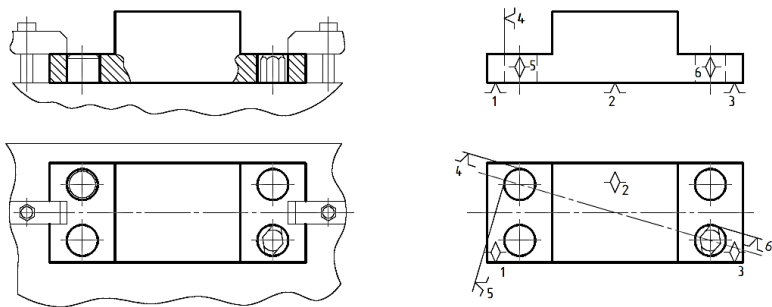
Схема базування корпусної деталі по площині і двох отворах.
